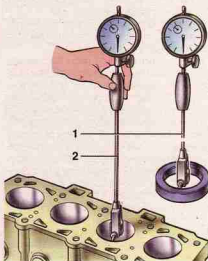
Измерение цилиндров нутромером: 1 — нутромер; 2 — установка нутромера на ноль по калибру 67.8125.9502
